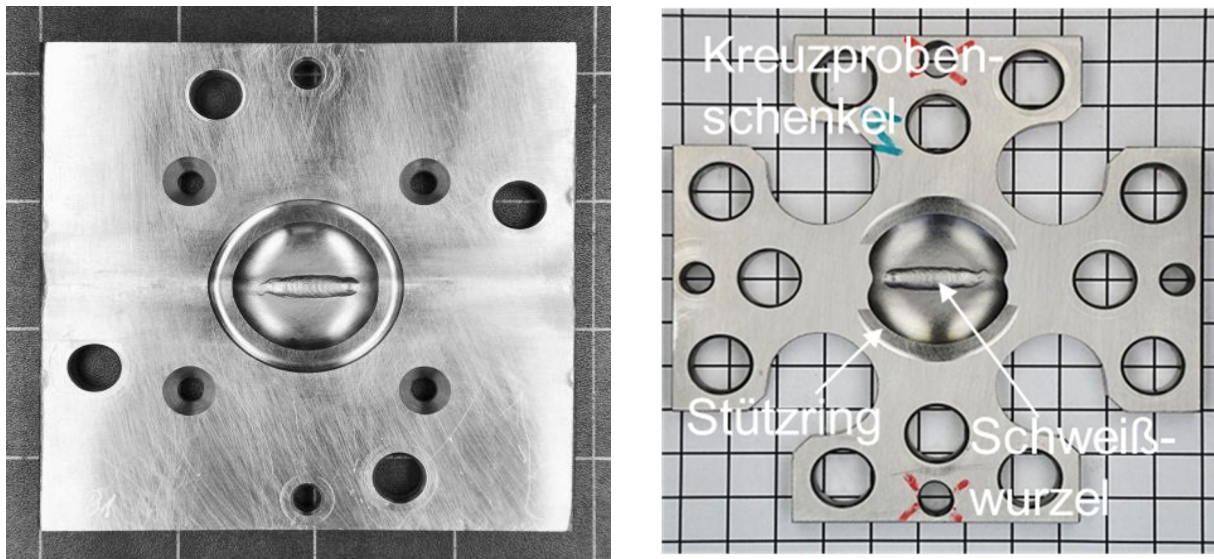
Kreuzproben mit unbearbeiteter Schweißnaht; Links: geschweißter Rohling; Rechts: nachbearbeitet Kreuzprobe
